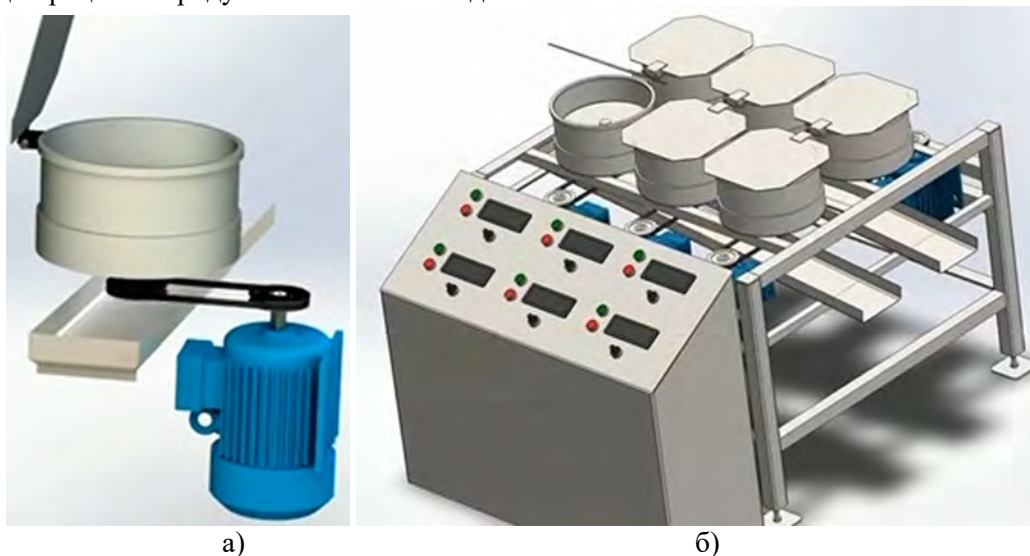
Зовнішній вигляд електропривода обкатувального барабана а) та загальний вигляд установки б)
